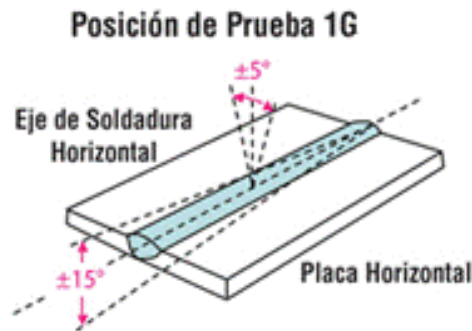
Soldadura de chapa a tope en posición 1G
